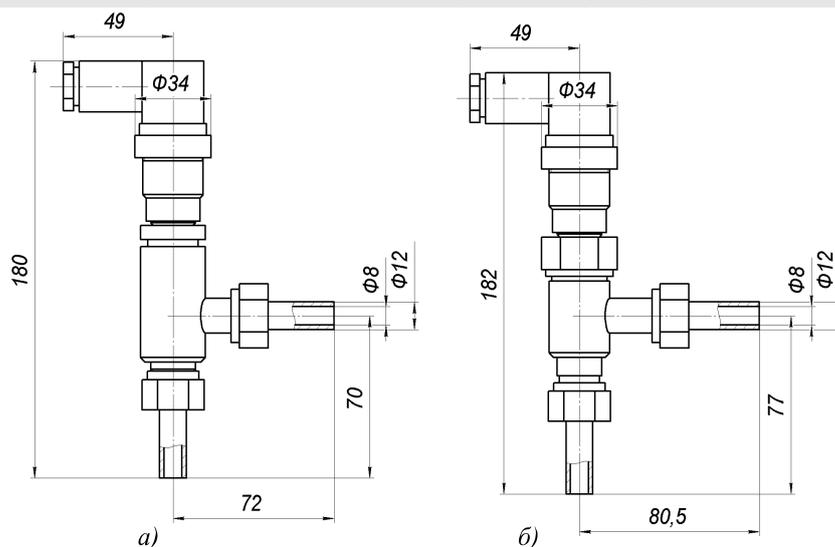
Габаритные и монтажные размеры проточного пассивного датчика ECS-1.15 (0..1000мСм/см) (а); ECS1.16 (0..1000мкСм/см) (б)
